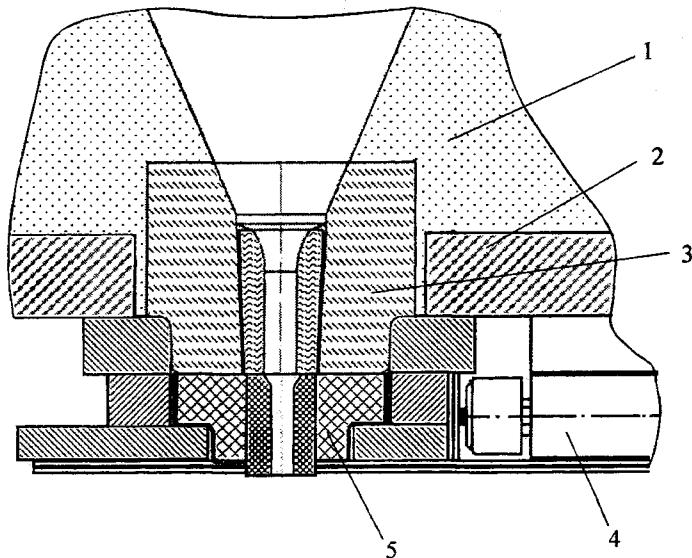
Схема разливочного узла промежуточного ковша для разливки открытой струёй:
